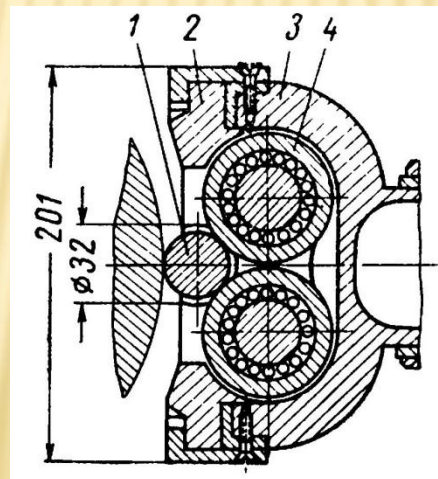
Головка пристосування з самоустановним роликом циліндричної форми
